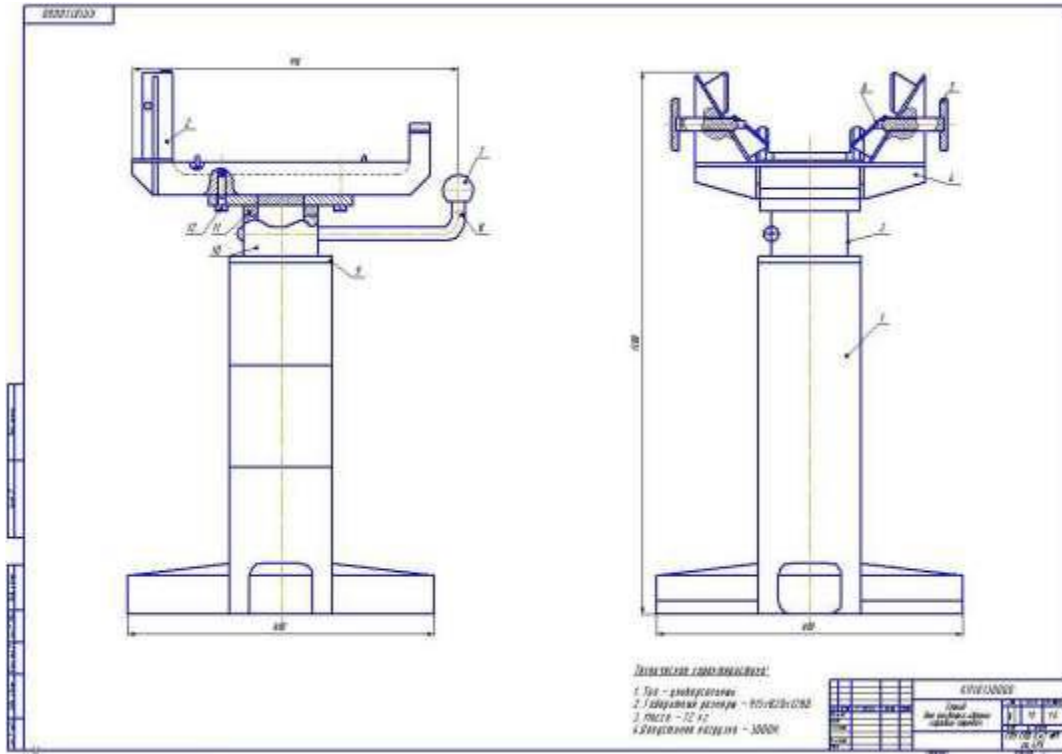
Пример общего вида станда для разборки-сборки коробок переключения передач
